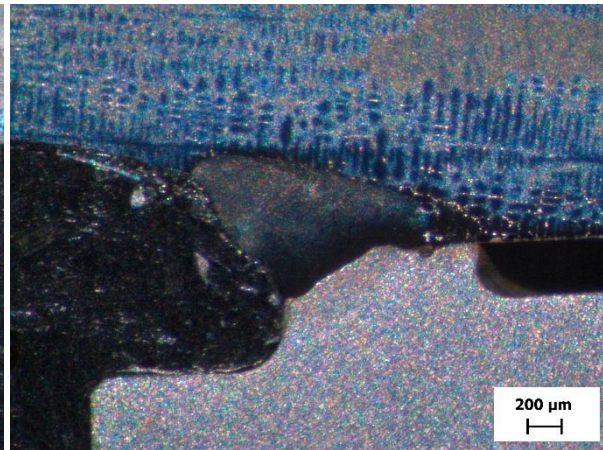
Inconel 713C+42CrMo4 leptadlo Adler
